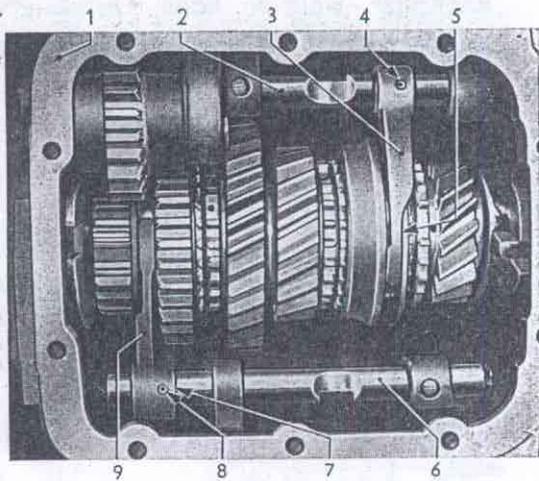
Anordnung der Schaltgabel im Getriebegehäuse
